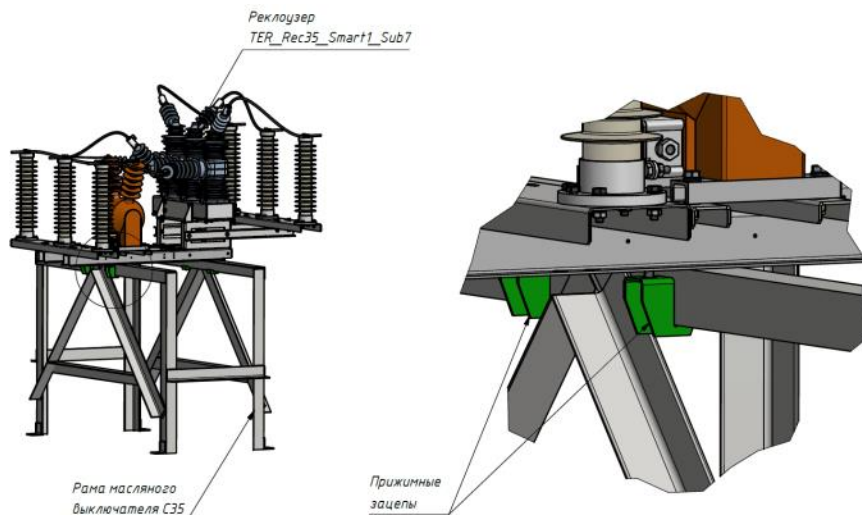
Крепление к раме масляного выключателя прижимными зацепами
